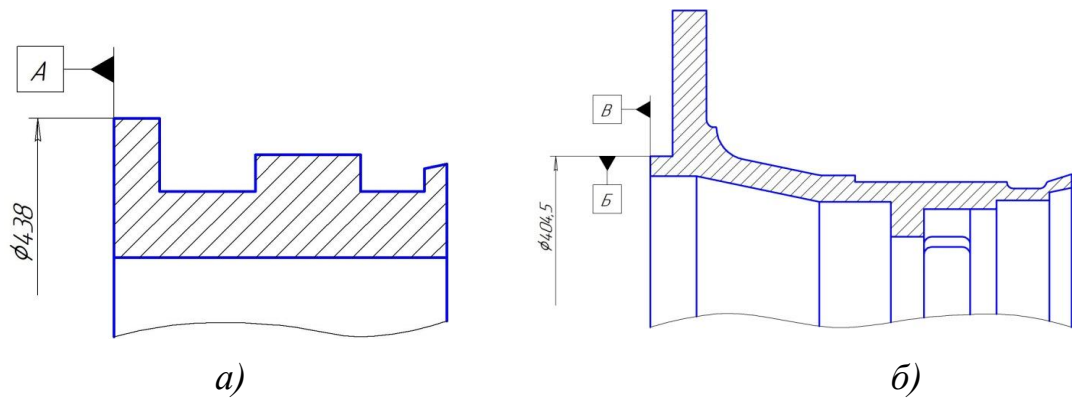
Ескізи баз.(а – чорнова база, б – чистова база)
